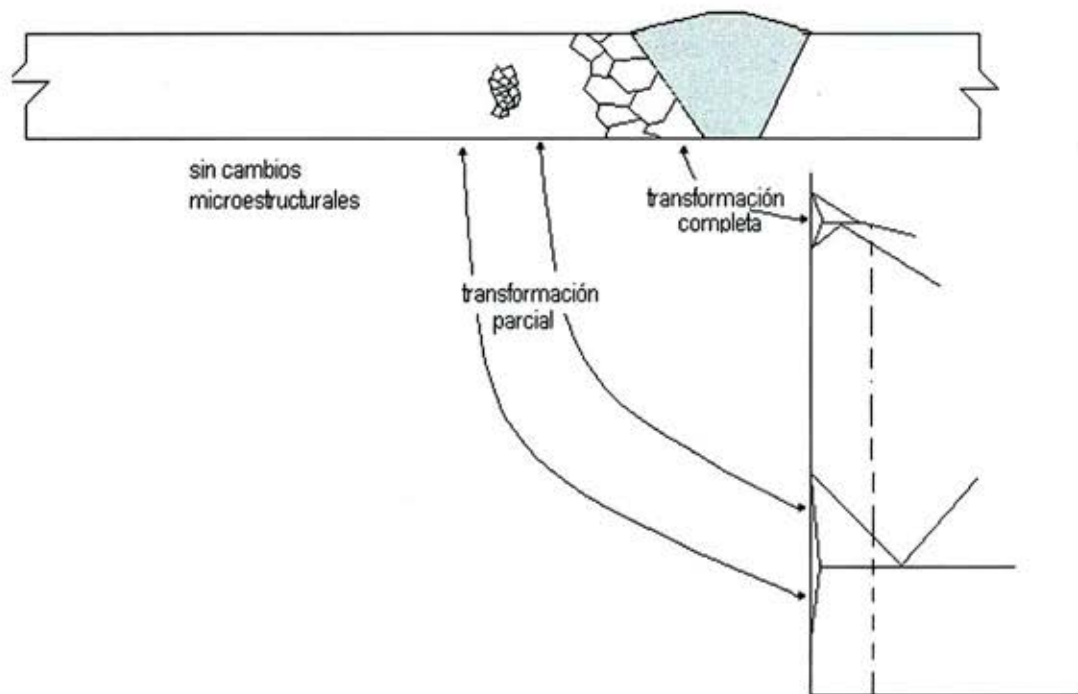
Zonas importantes en un cordón de soldadura
